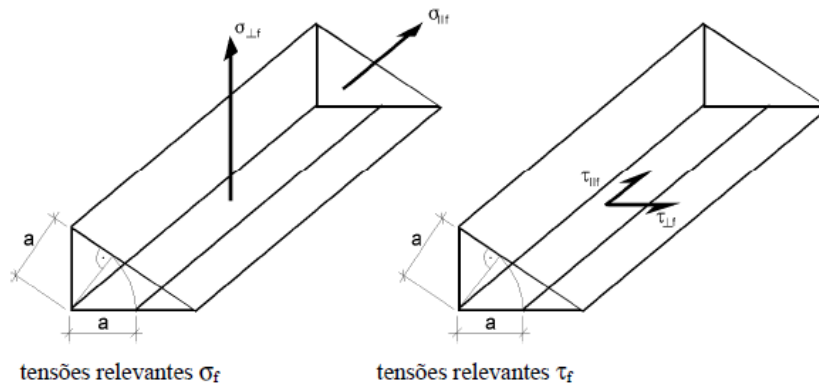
Direção das tensões nos cordões de soldadura
